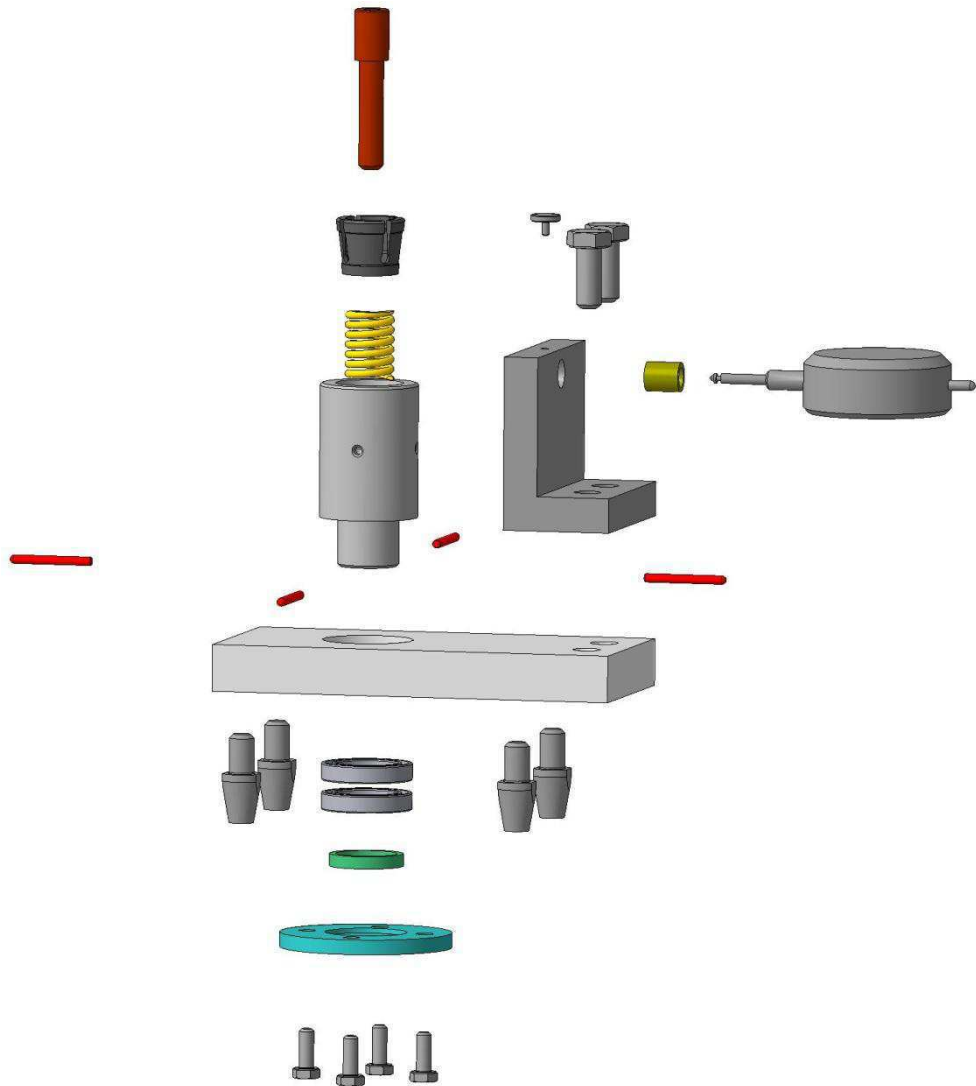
Разнесение 3D модели контрольного приспособления на детали
